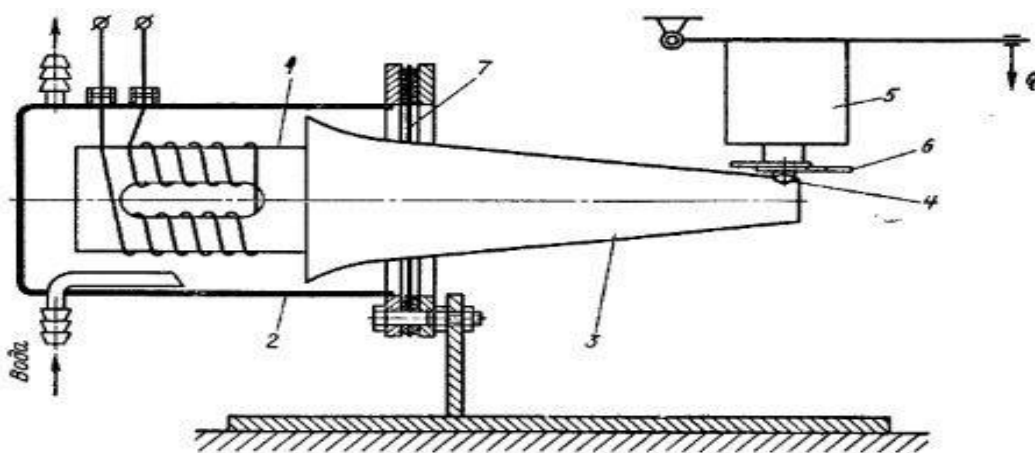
Схема установки для точечной сварки ультразвуком
